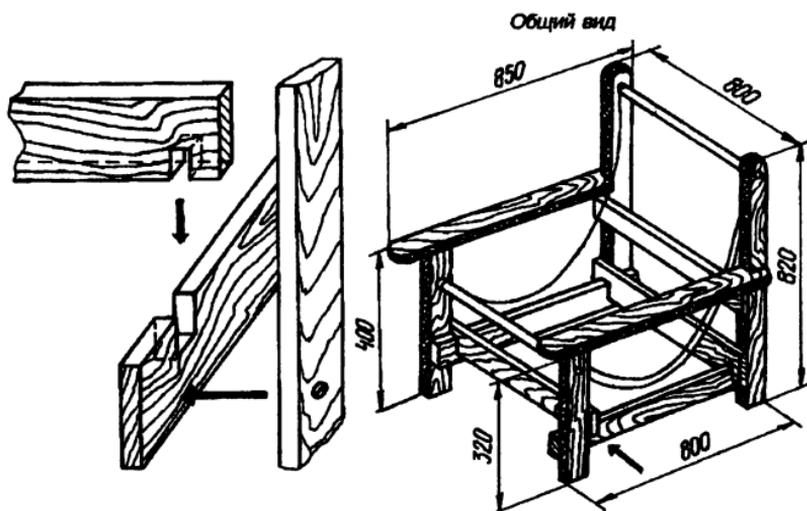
Дачное кресло. Общий вид и сборочный чертеж
